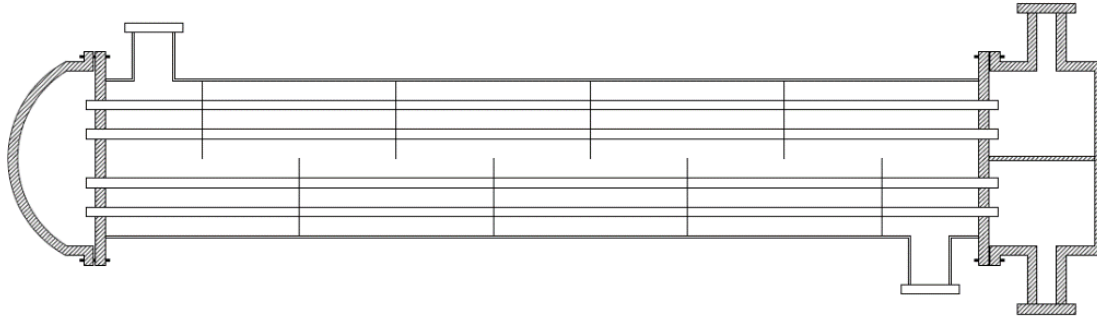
Intercambiador 1-2 de cabezal fijo.
